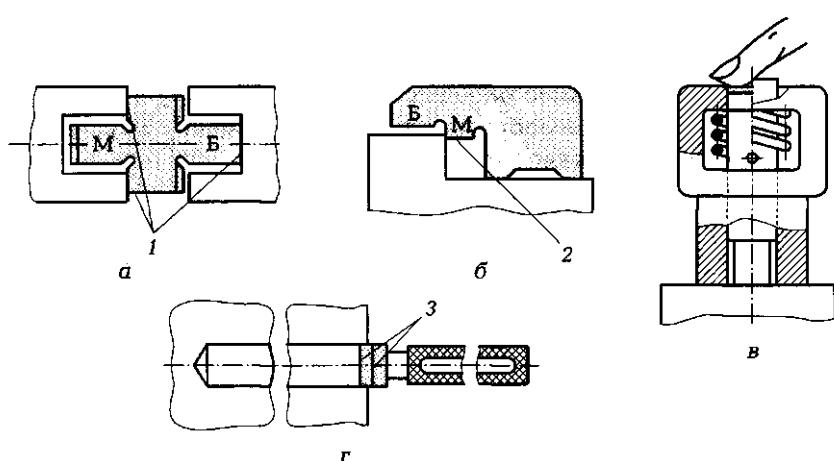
Калибры для контроля глубин и высот уступов:
